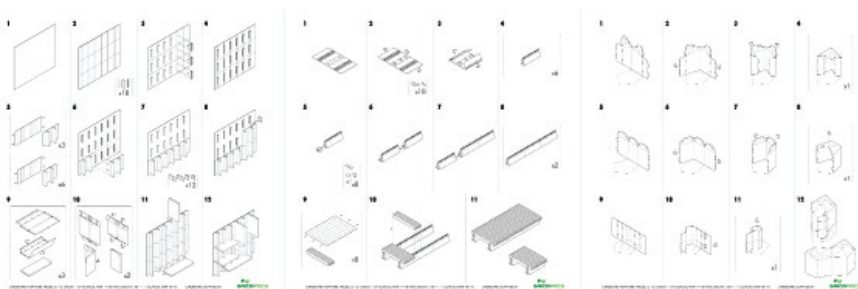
Instrucciones de montaje para los elementos de mobiliario diseñado
